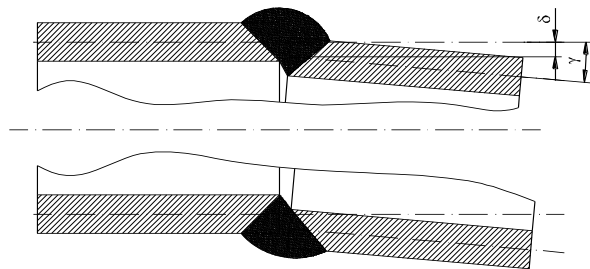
Параметрическое представление сечения сварного шва для труб, повернутых и смещённых относительно друг друга.
